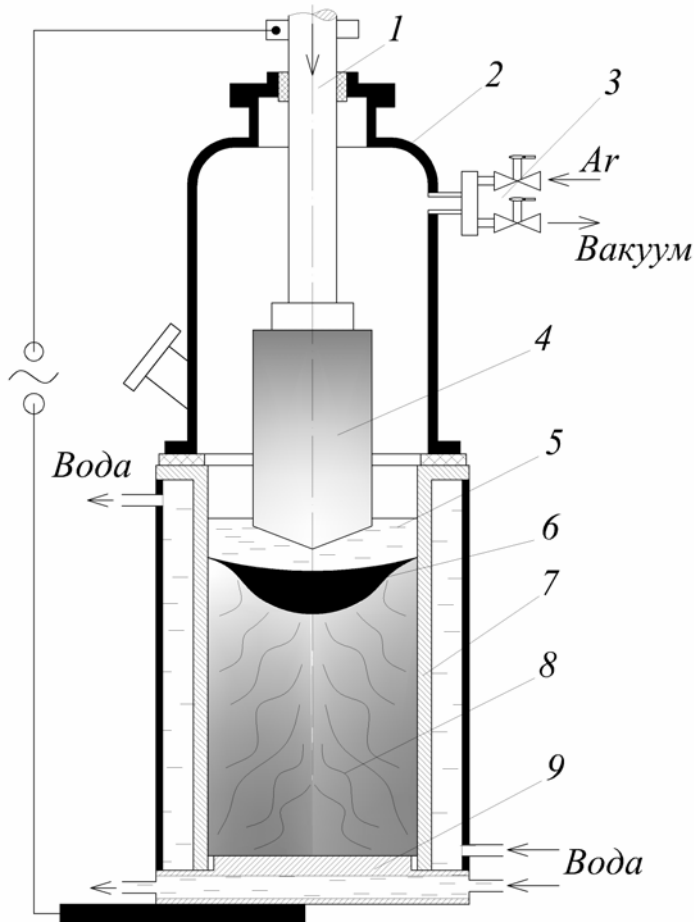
Схема процесу ЕШП титану: 1 – шток; 2 – вакуумна камера; 3 – газовий затвор; 4 – витратний електрод; 5 – шлакова ванна; 6 – металева ванна; 7- кристалізатор; 8 – зливоч; 9 – піддон.
